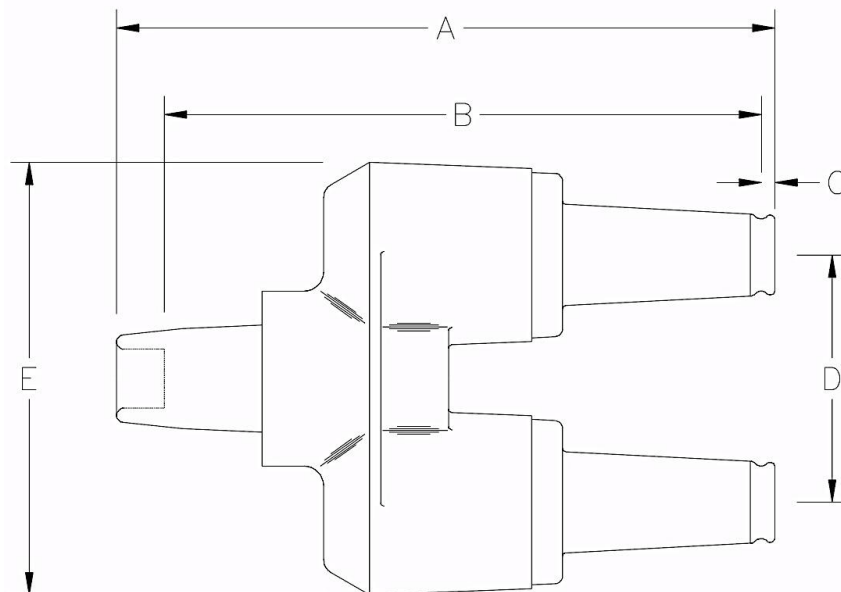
Dimensiones de boquilla tipo inserto doble, [12].
